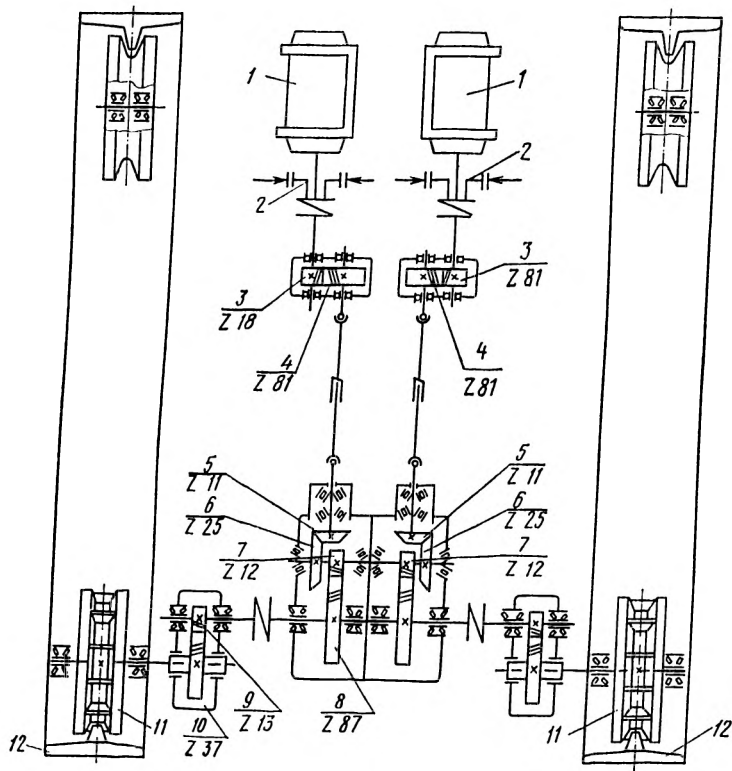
Кинематическая схема механизма передвижения крана СКГ-40А:
